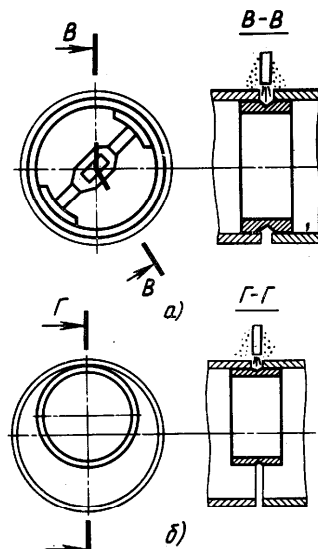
Флюсомедные подкладки для сварки кольцевых швов: а - неподвижная; б - перекачиваемая
